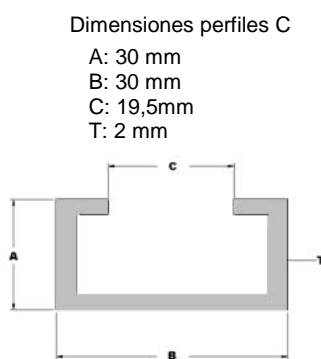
Sistema de suspensión del conducto y junta transversal METU-System.
